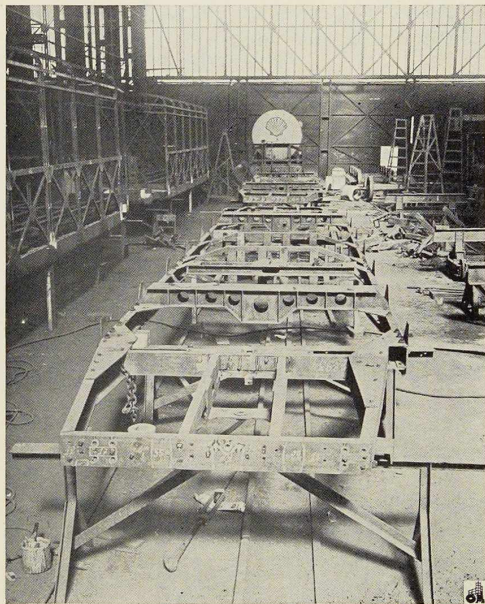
Vue d'ensemble du châssis en cours d'assemblage.
